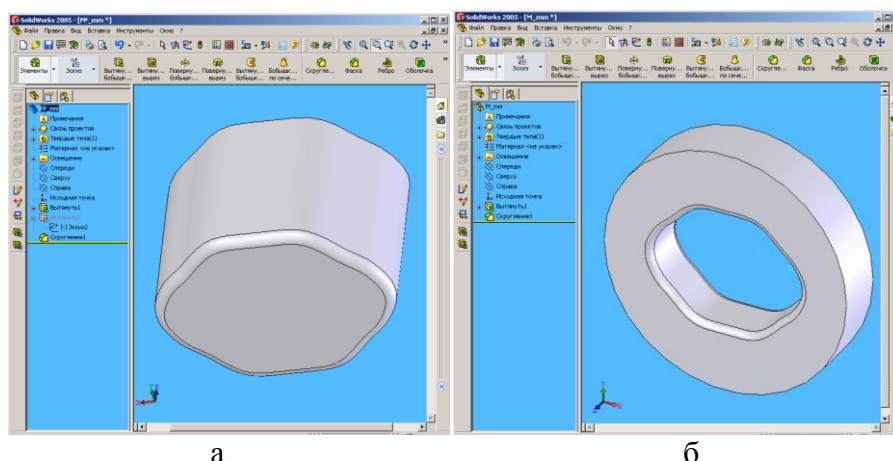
Твердотільні моделі: а – пуансона і б– матриці для першого переходу витягування коробчастого виробу.
